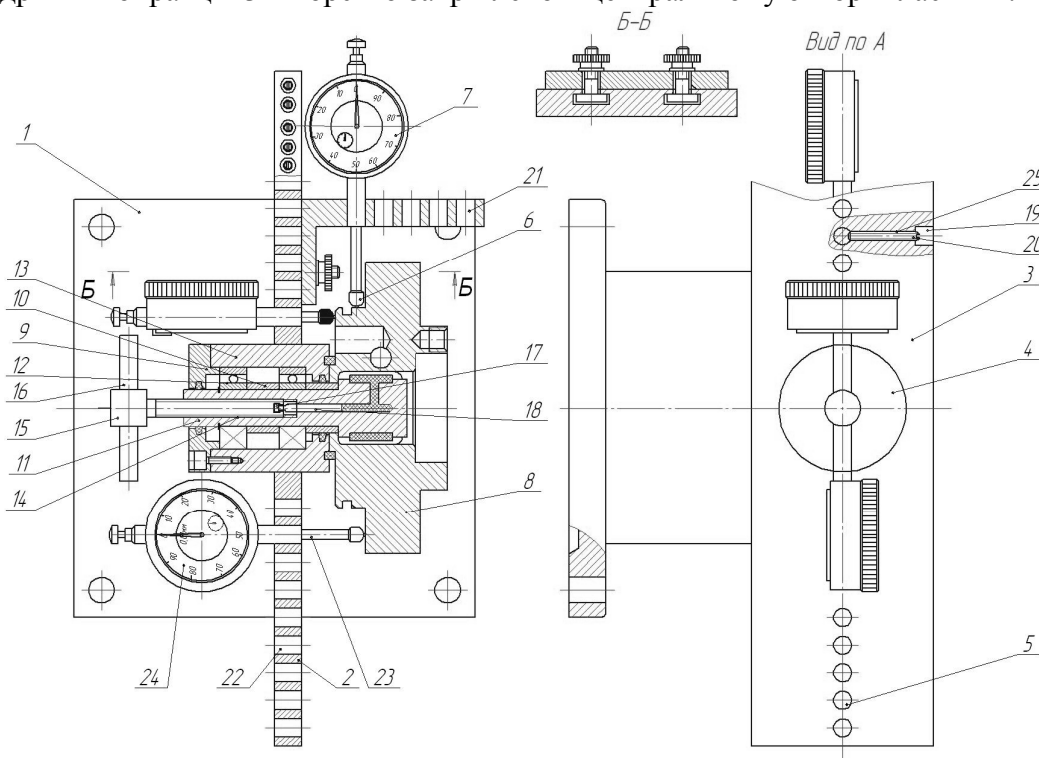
Контрольний пристрій для заміру конструктивних параметрів корпусних деталей
